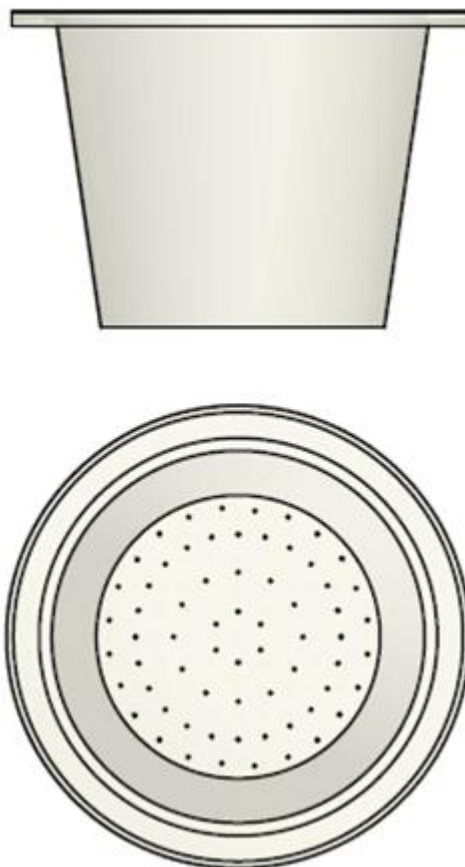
Planta y alzado de la cápsula de Marcilla L'Arome. [SAR11]
